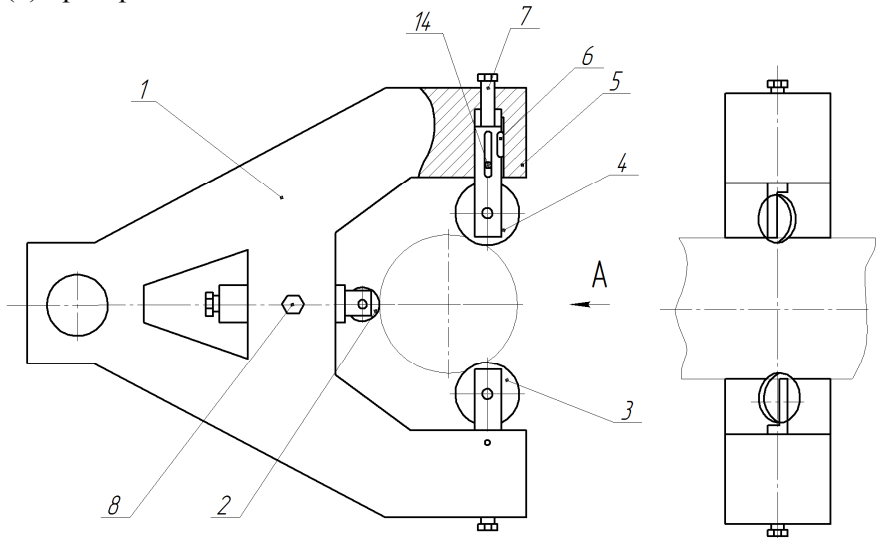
Пристосування для поверхнево-пластичної деформації робочих поверхонь деталей машин
